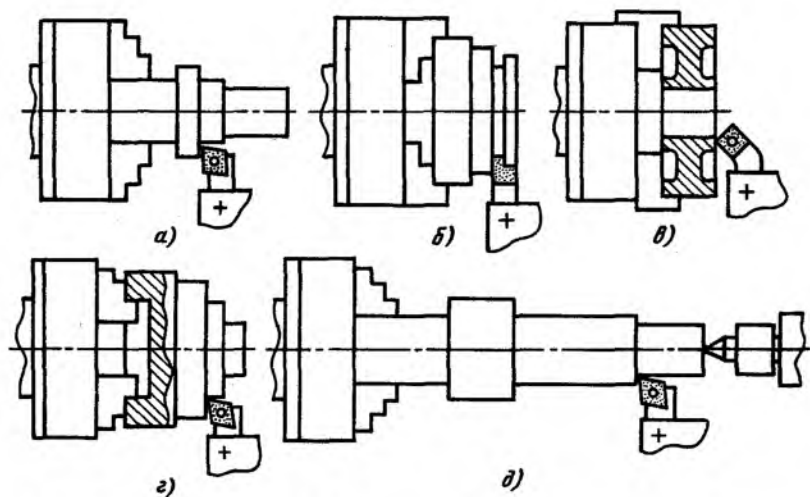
Способы крепления в трехкулачковом самоцентрирующем патроне:
